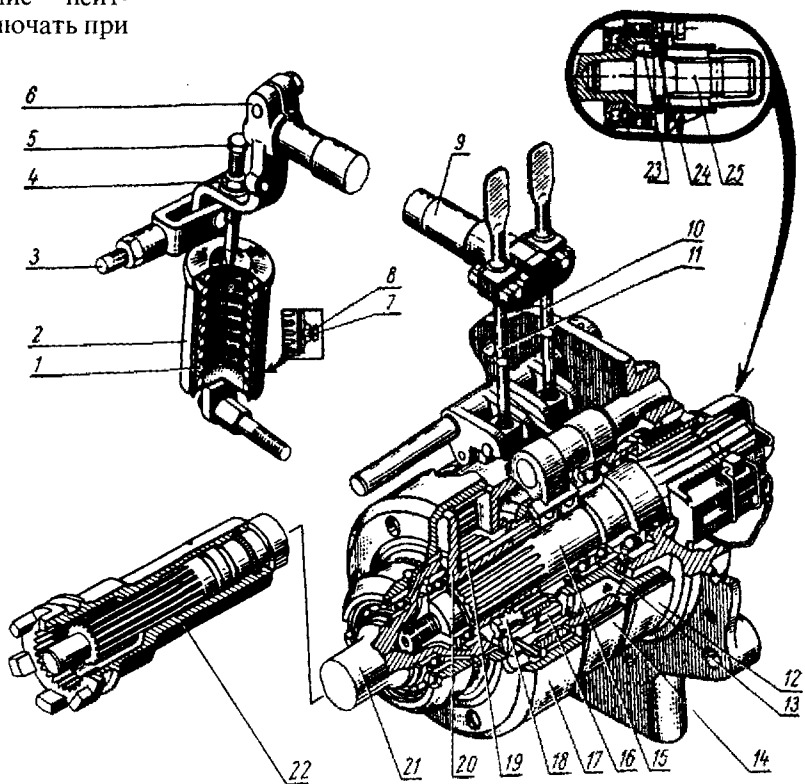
Планетарный редуктор заднего ВОМ тракторов семейства МТЗ: 1 – пружина цилиндрическая; 2 – стакан; 3 – тяга; 4 – контргайка; 5 – болт упорный; 6 – рычаг валика управления; 7 – болт стопорный; 8 – гайка; 9 – валик управления; 10, 11 – винты регулировочные; 12, 14 – лента тормоза с фрикционной накладкой; 13 – барабан включения ВОМ; 15 – вал заднего ВОМ; 16 – ось сателлита; 17 – шестерня коронная; 18 – сателлит; 19 – шестерня солнечная; 20 – водило (в сборе с тормозным барабаном); 21 – вал коронной шестерни; 22 – муфта переключения привода; 23 – ролик; 24 – стопорное кольцо; 25 – сменный хвостовик
